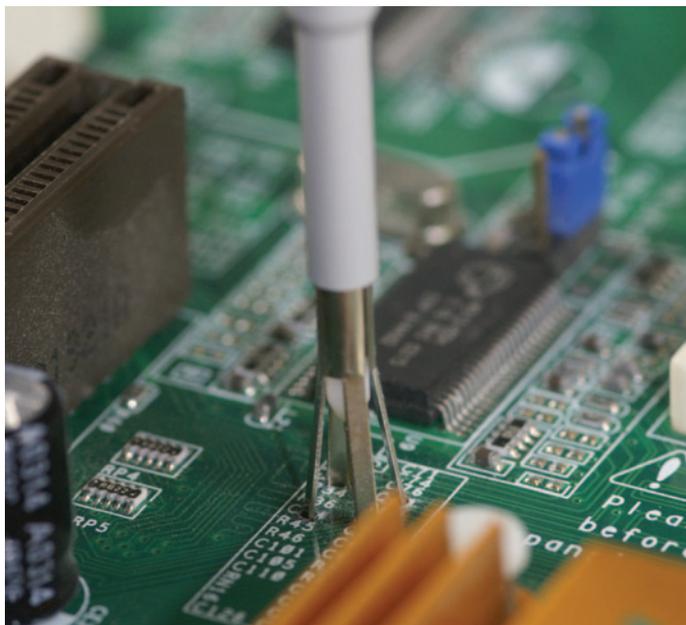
Keysight N2885A PCB 适配器插座作为测试点焊入印刷电路板 (PCB)，以便最大限度地降低接地电感和提高信号保真度。该套件包括 25 个插座。
